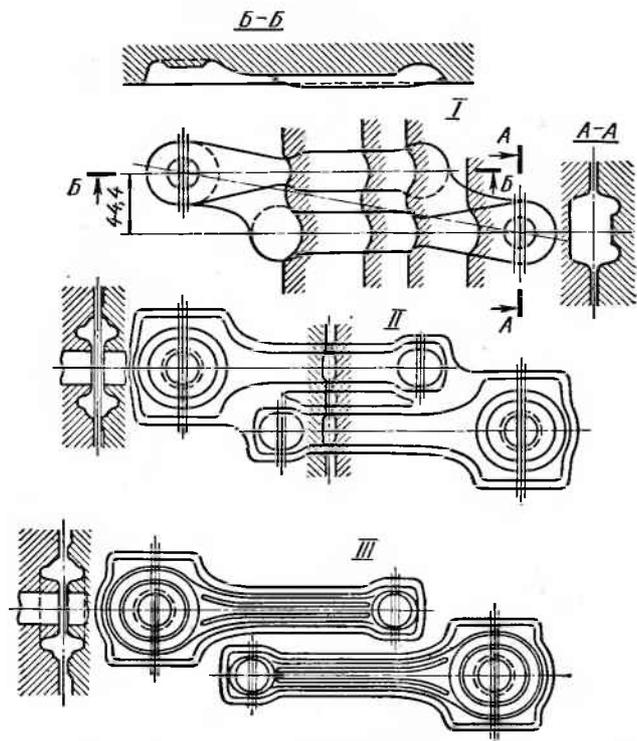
Ручьи штампа КГШП для поковки шатуна:
